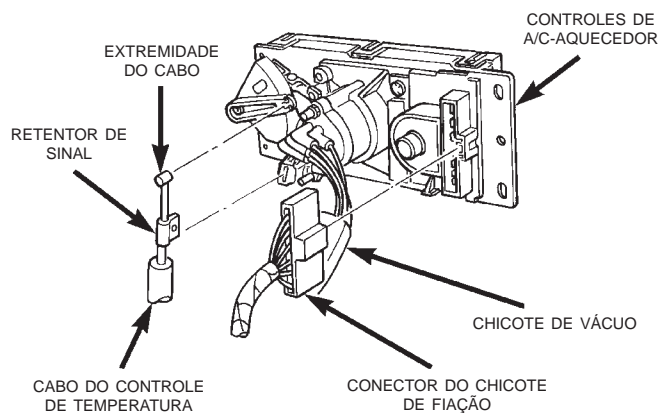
ajustagens do Controle de A/C-Aquecedor
